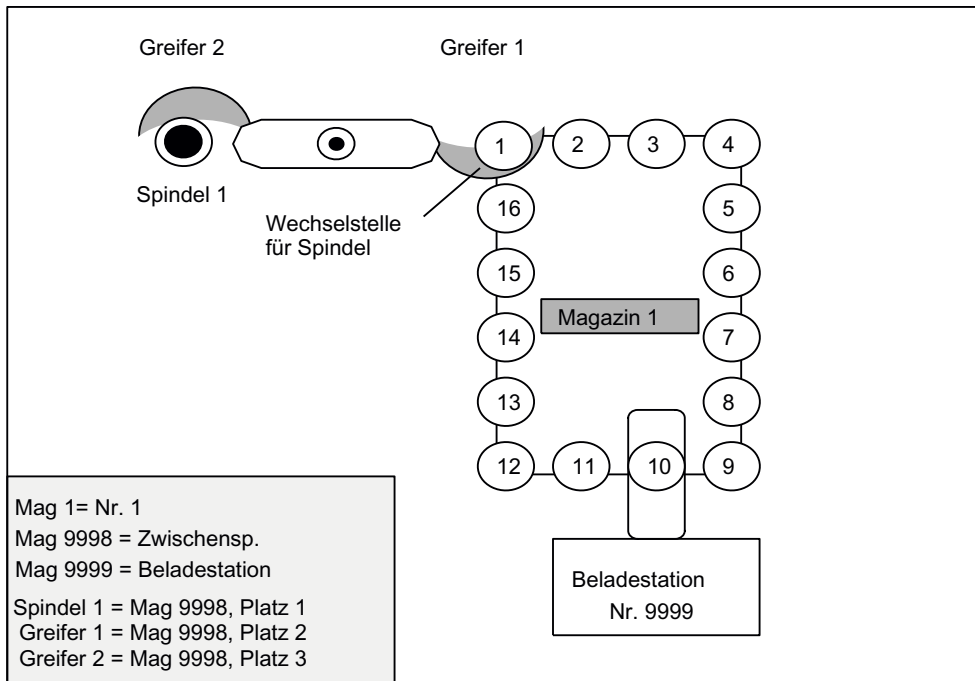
Werkzeugmaschine mit einem Kettenmagazin
